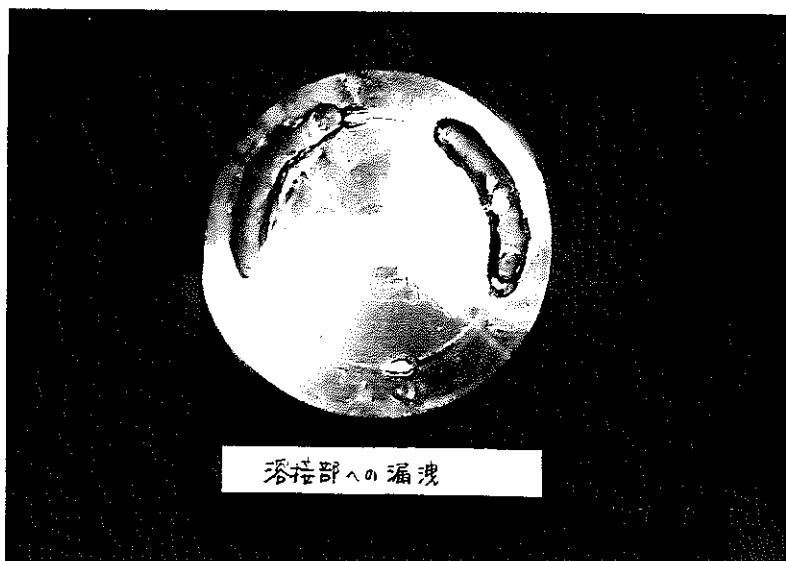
(1/3) 非定常時の溶接停止部外観
